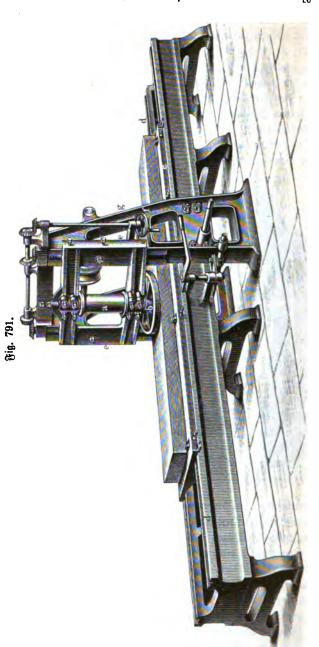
Die Messer ragen aus ber unteren Fläche ber auf ber senkrechten Spinbel a besestigten Scheibe b hervor, die durch einen auf a gestührten halbgeschränkten Riemen schnell umgedreht wird, während das zu hobelnde Holz auf der Tischplatte c durch geeignete Spannvorrichtungen besestigt ift. Wenn diese in den prismatischen Führungen des Bettes a geleitete Tischplatte in der von den Metallhobelmaschinen her bekannten, in der Figur nicht näher erläuterten Art langsam verschoben wird, so wird durch die Messer in der schneiden der Scheibe b die obere Fläche des Holzes in der schon oben besprochenen Weise abgerichtet. Die Messerwelle sindet hierbei ihre Lager in einem Rahmen e, der an den senkrechten Führungsbahnen des Gestelles g vermittelst der beiderseits angebrachten Schraubenspindeln durch Umdrehung des Handrades f sehr genau verstellt werden kann, so daß man hierdurch nicht nur die Stärke des abzunehmenden Spanes in der Hand hat, sondern auch den jeweiligen Dicken verschiedener Hölzer entsprechend die Stellung der Messerschiebe bestimmen kann.
